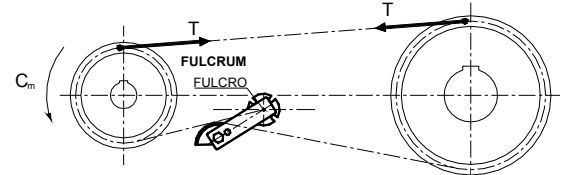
MONTAGGIO ERRATO! / WRONG ASSEMBLY / FALSCH MONTAGE (NICHT EMPFOHLEN!)
